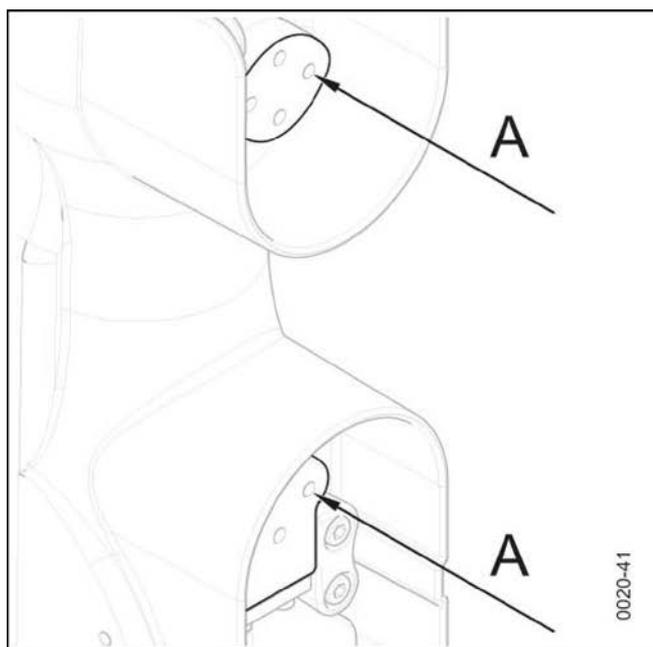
Глубина ввинчивания в верхний и нижний контакт
